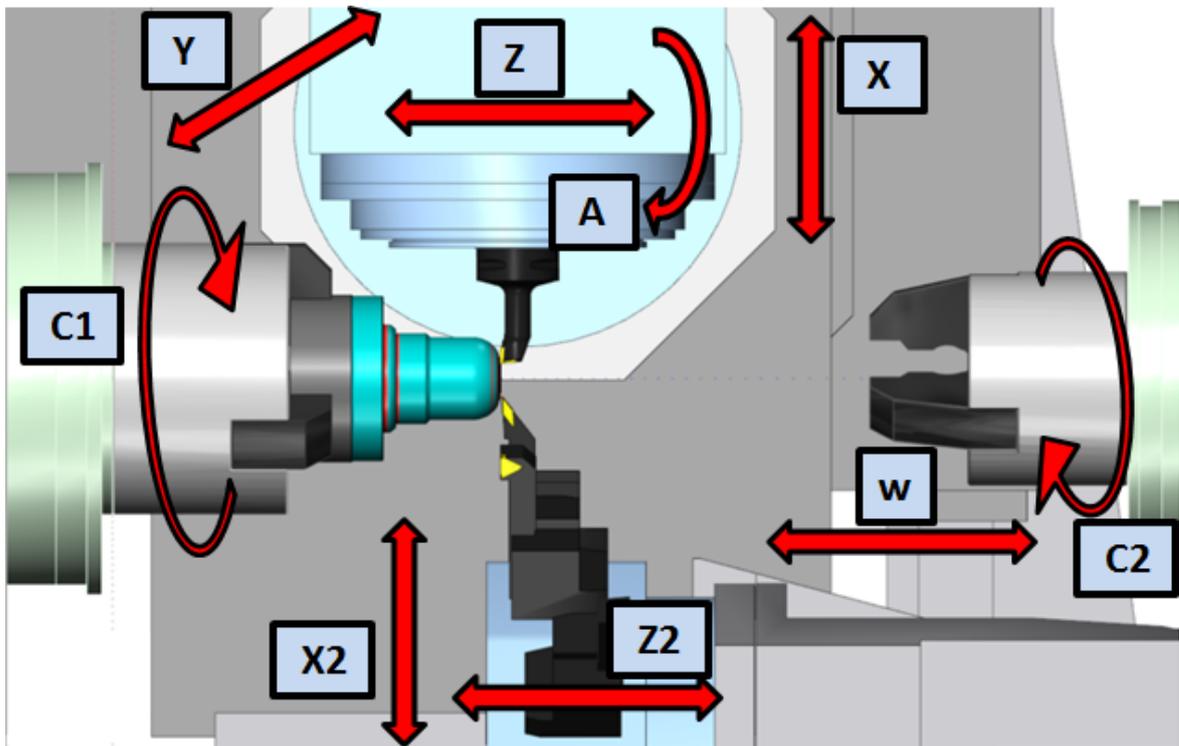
Кинематическая схема 9-ти координатного токарно-фрезерного ОЦ
